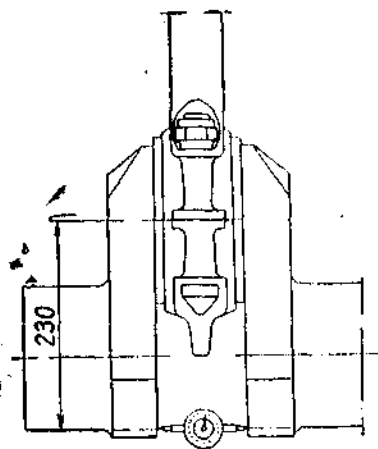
Установка на кривошипе приспособления для измерения расхождения шек коленчатого вала
